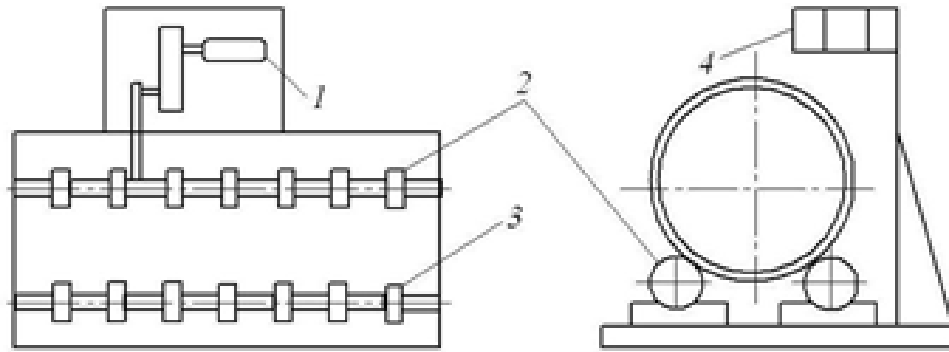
Стенд для автоматичного зварювання колонної апаратури:
